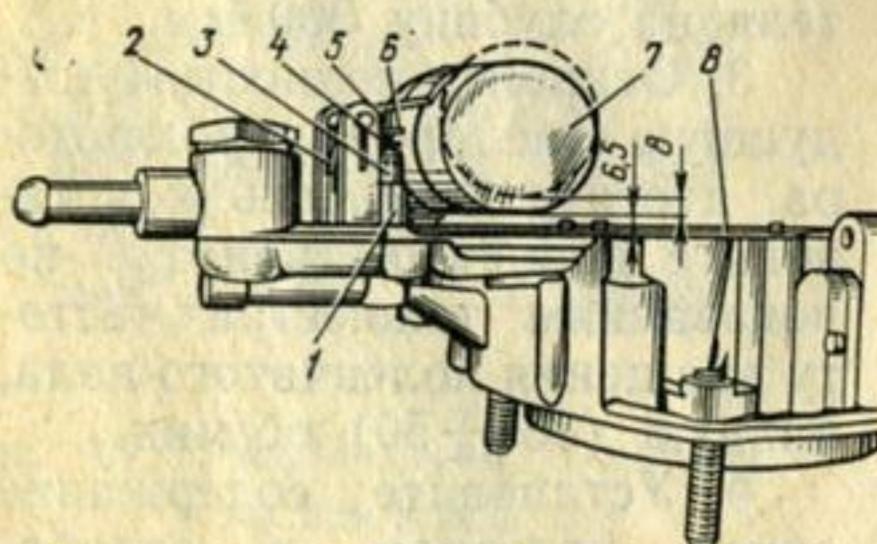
Проверка установки поплавка на крышке поплавковой камеры карбюратора:
